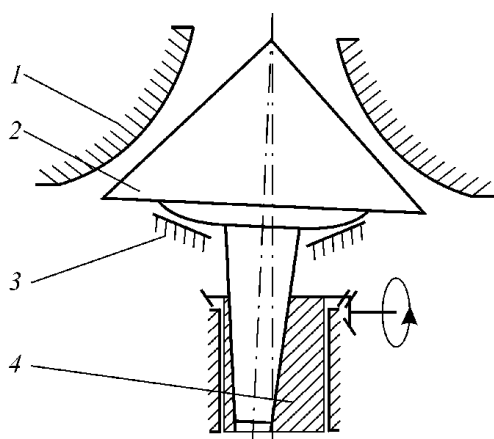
Схема конусных дробилок среднего и мелкого дробления: 1 — неподвижный конус; 2 — подвижный конус; 3 — сферическая опора; 4 — эксцентриковый стакан
